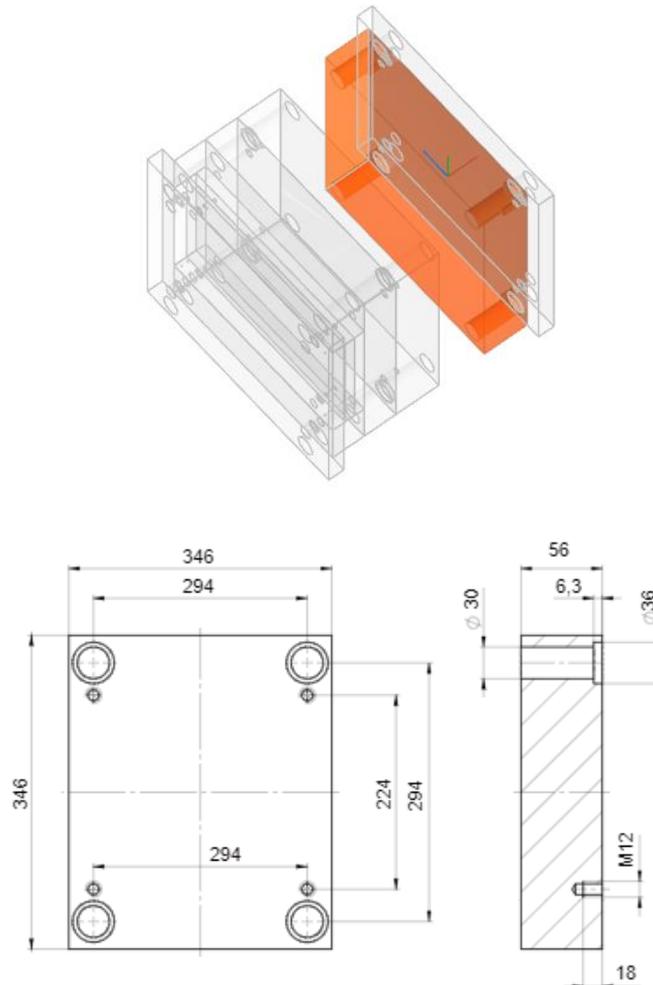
Dimensiones de la placa de la cavidad de la parte fija, HASCO.
